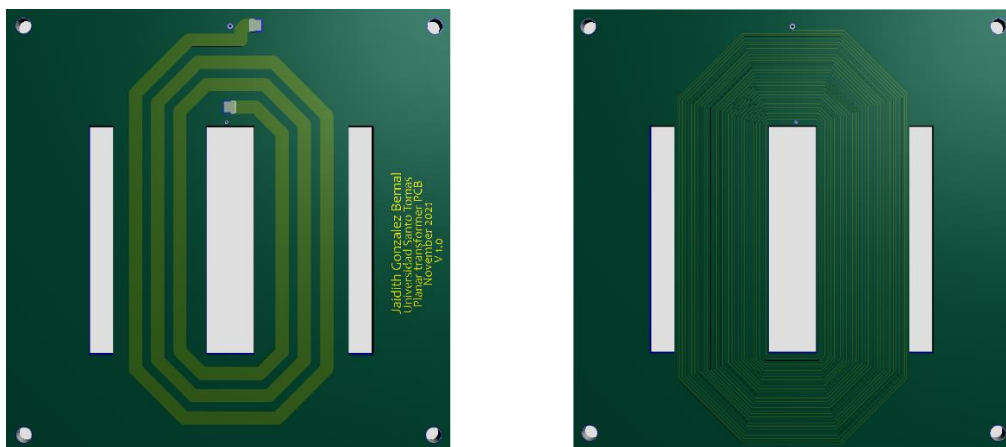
Vista previa de la PCB. Bobinado primario (izquierda), bobinado secundario (derecha). Fuente: Autor
